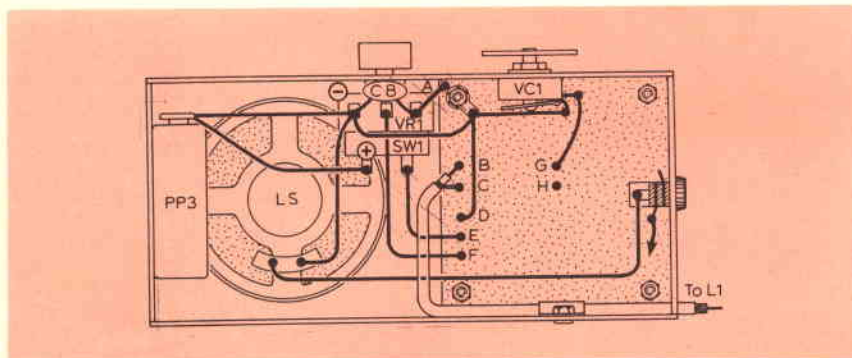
Questa figura chiarisce una delle possibili soluzioni per inserire i diversi componenti all'interno dell'involucro, che viene qui illustrato visto dal retro, senza il coperchio.
